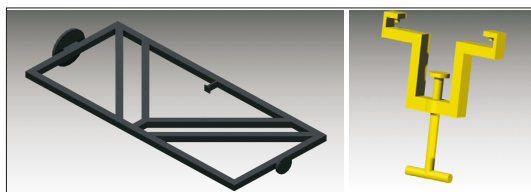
Ogólny widok uchwytu spawalniczego wraz z zamocowanymi elementami kolana
